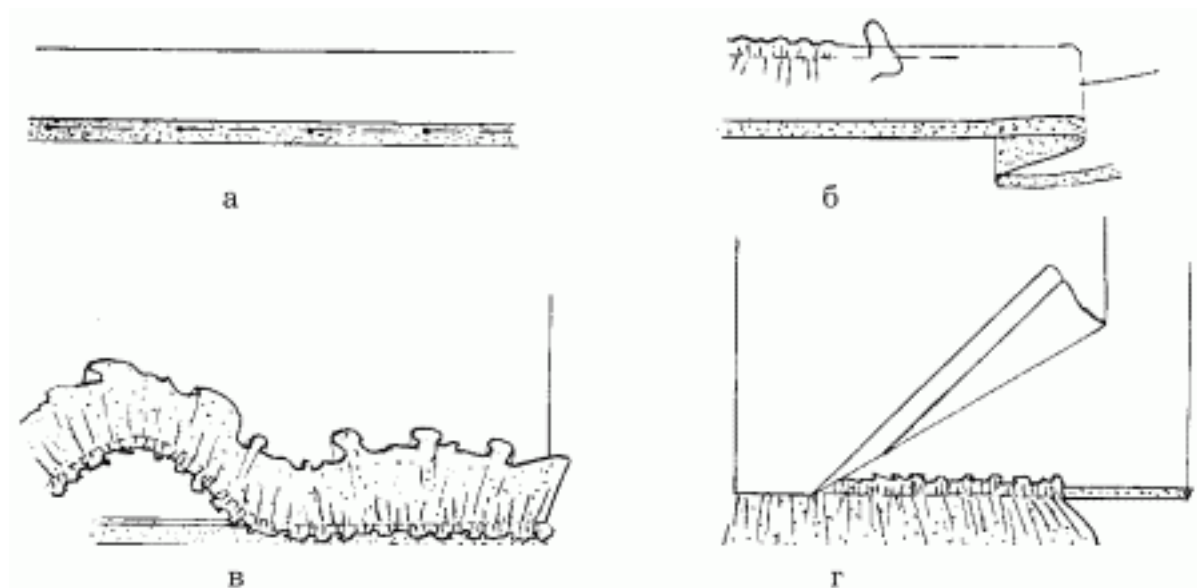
Последовательность изготовления оборки с подкладкой, оформленной руликом: а – стачивание основной и подкладочной деталей; б – приспособивание всей оборки; в – приметывание оборки к ткани основной детали; г – притачивание оборки к изделию между основной деталью и подкладкой.
